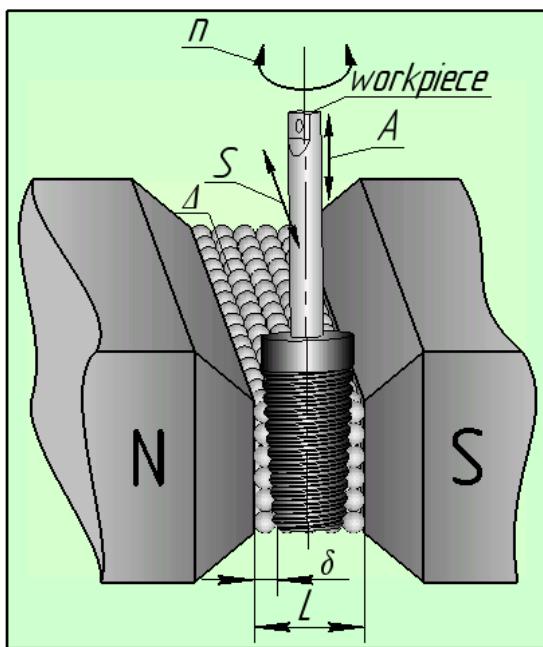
Схема магнитно-абразивной обработки наружных резьбовых поверхностей
